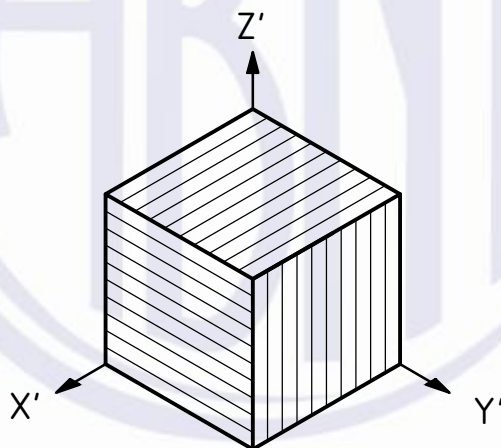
Hachura indicando planos paralelos aos planos de coordenadas
